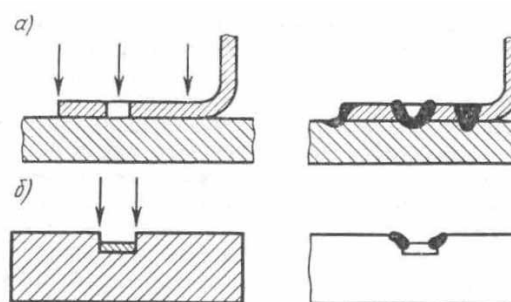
Типы сварных соединений тонких плоских деталей с массивными деталями
